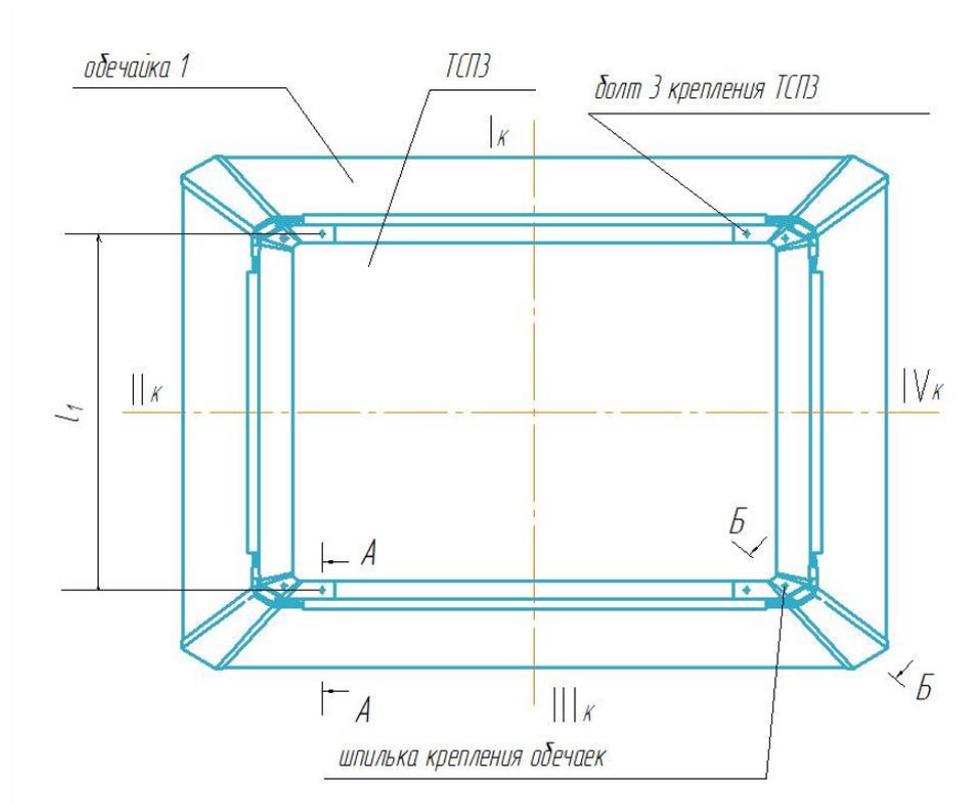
Конструкция корпуса в зоне установки болтов
